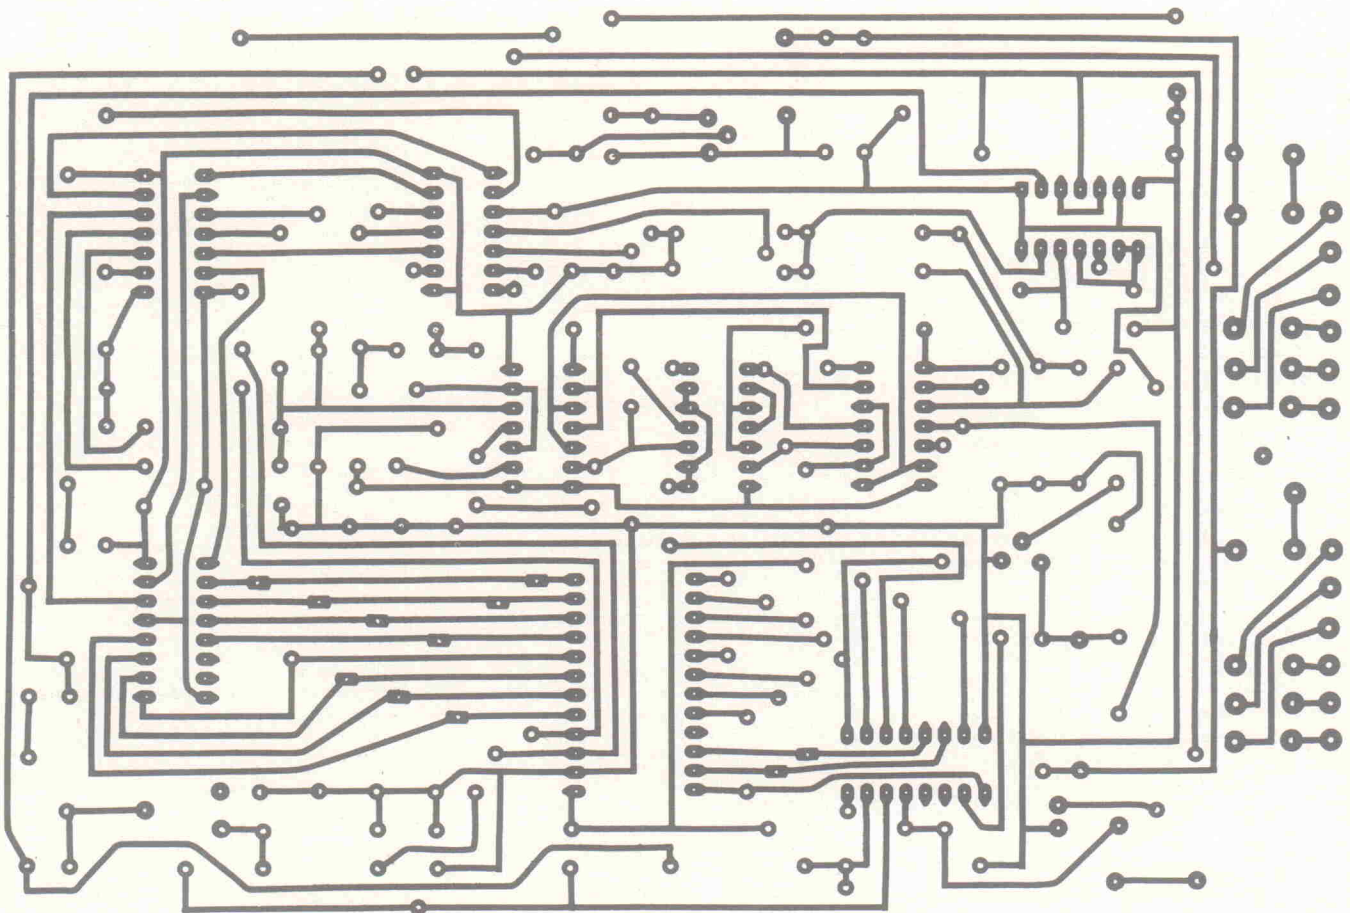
Das Layout der Hauptplatine. Wer beim Bohren kein Loch ausläßt, vergißt auch keine Drahtbrücke.
